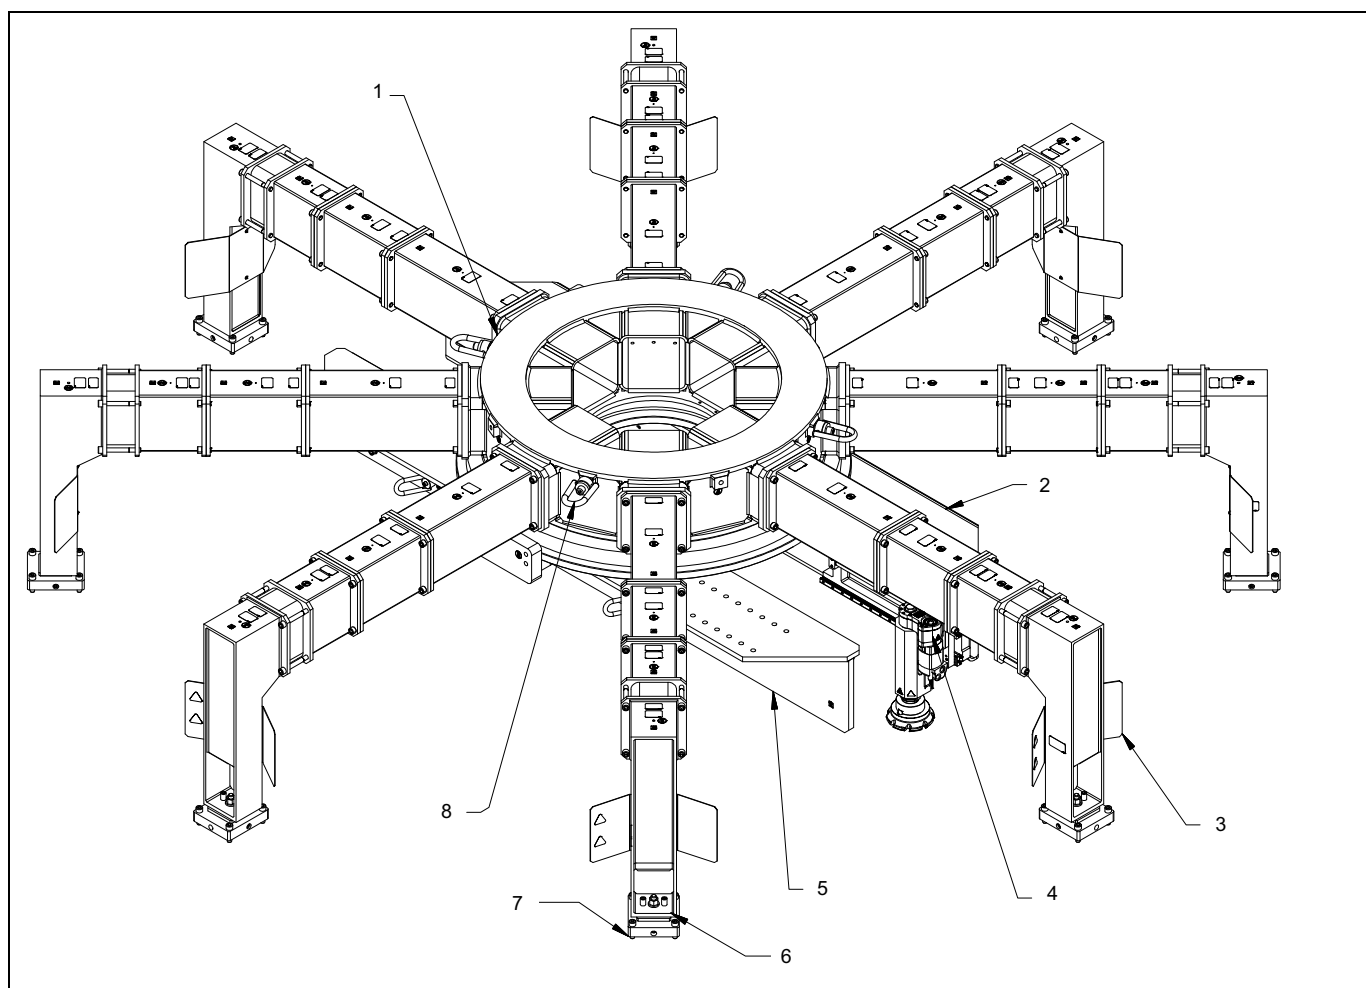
COMPOSANTS DE MONTAGE SUR DE
